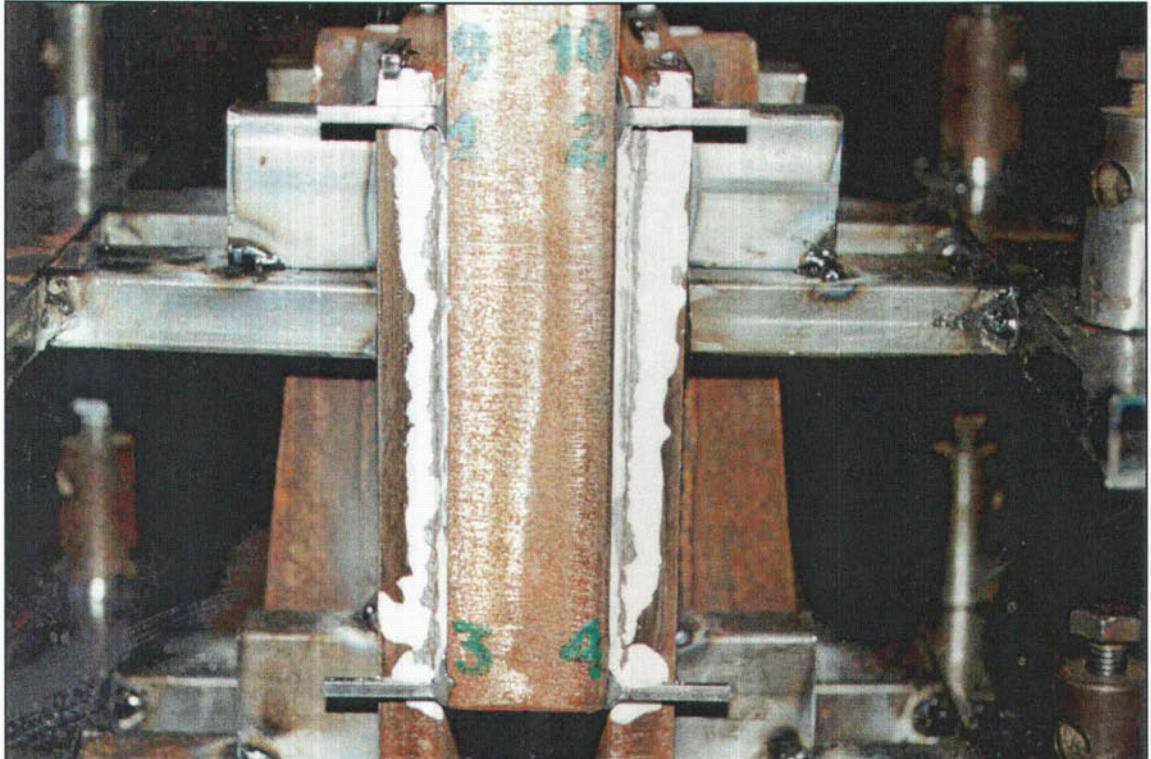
Detalle de la probeta 2S ya rota. Se observa en la fotografía la rotura de las soldaduras 1-3 y 2-4. La rotura nuevamente se produce por la sección de garganta de las soldaduras.
